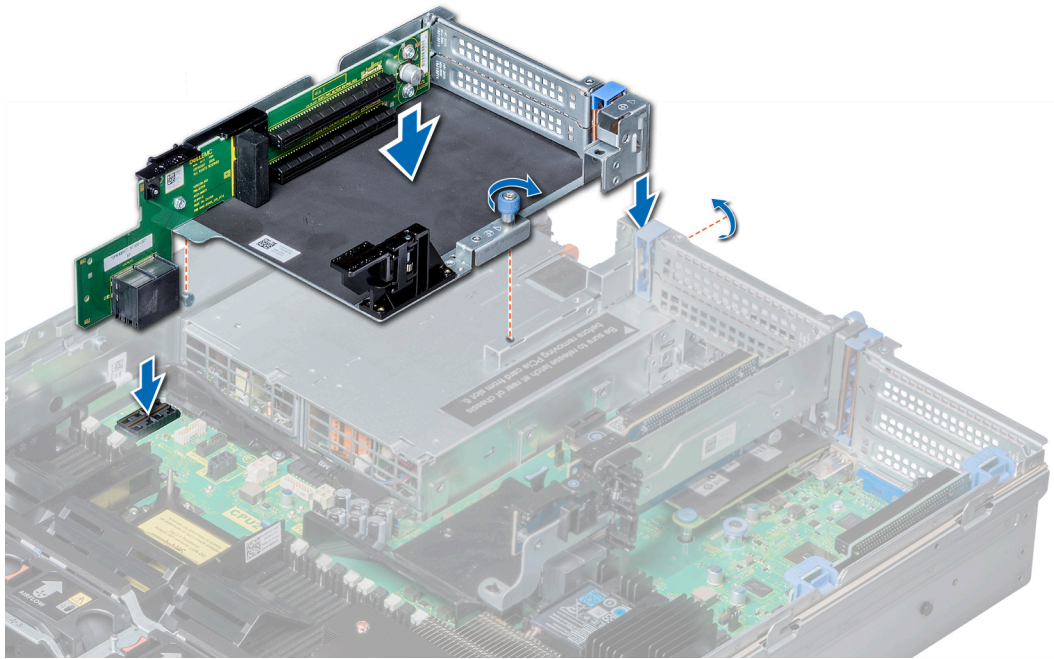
Installation de la carte de montage 3 pour carte d'extension
